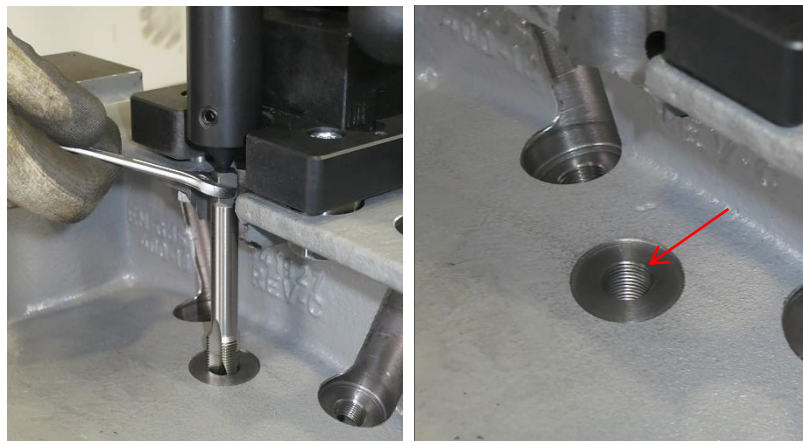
u 34: Übersicht Gewindeschneiden in BP1
